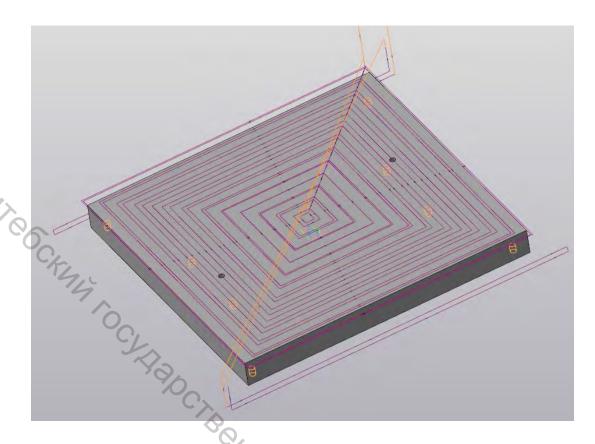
Траектория инструмента при черновом и чистовом фрезеровании заготовки во втором установе
